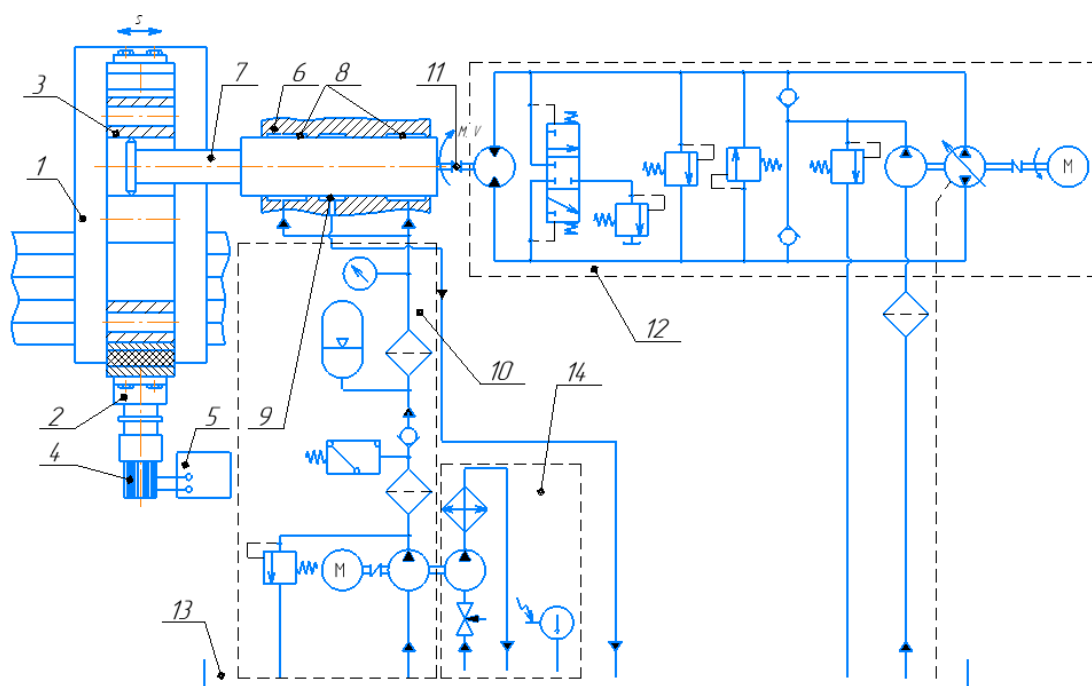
Комбінована схема установки для механічної обробки внутрішніх поверхонь отворів : 1 - стіл 1; 2 – оправка; 3 – деталь, що оброблюється; 4 - вібратор крутильних коливань; 5 - генератором коливань; 6 – передня бабка; 7 – різець; 8 – камери гідростатичного підшипника; 9 – гідравлічний привід гідростатичних опор; 10 – камери зливу робочої рідини; 11 – муфта; 12 – гідравлічний привід; 13 – гідробак; 14 – блок охолодження
